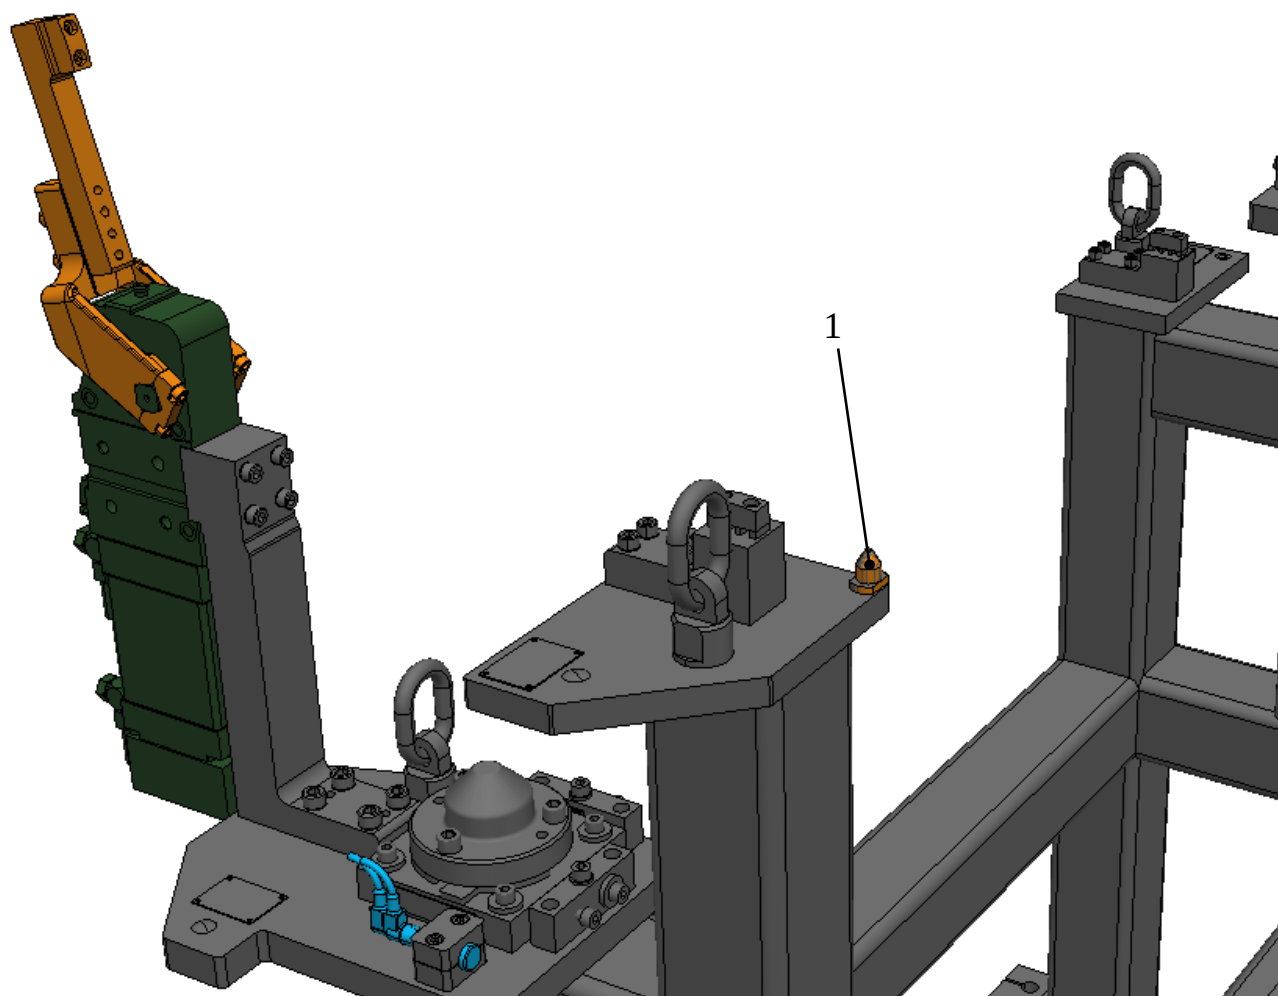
Положение калибровочного конуса на перекладной станции 5076
